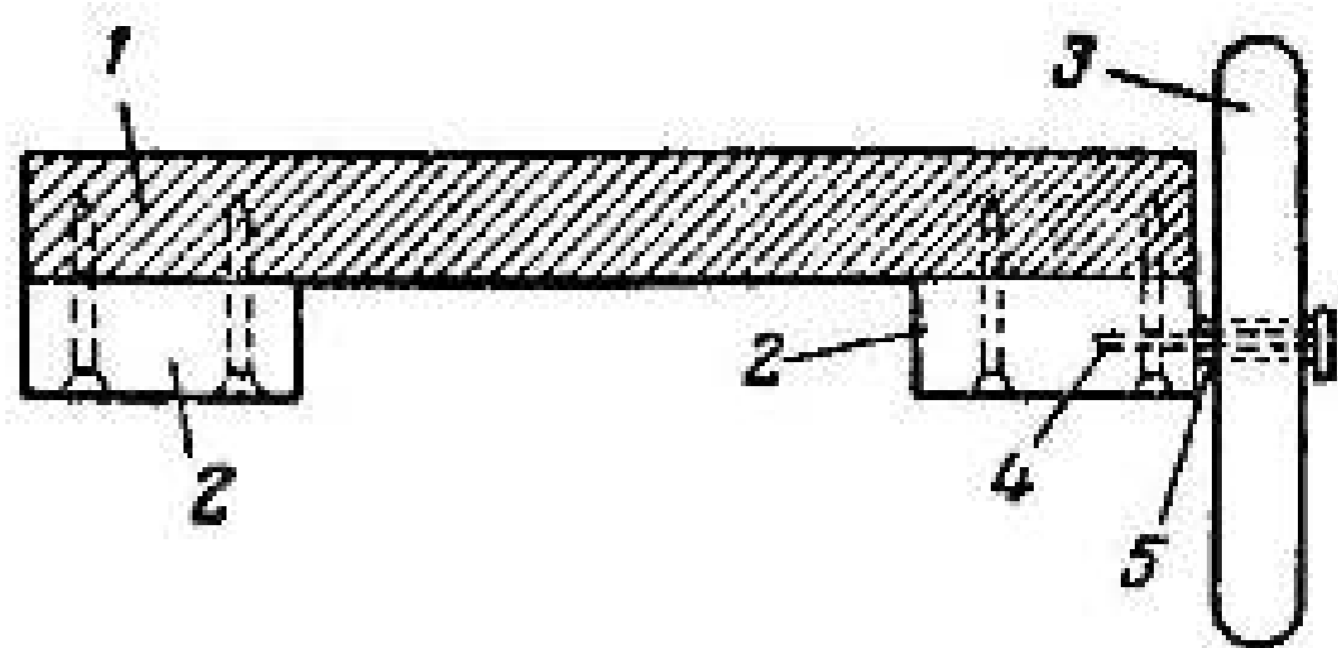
Монтаж передней — неведущей оси с помощью бобышек: 1 — рама модели; 2 — бобышка; 3 — колесо; 4 — ось колеса; 5 — шайбочка
